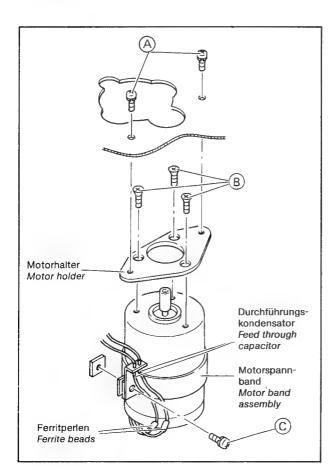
Wickelmotorausbau Fig. 2-9 Reel motor replacement
